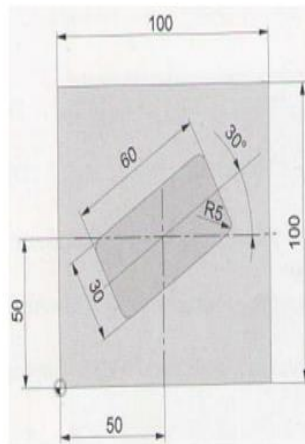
Эскиз корпуса для программирования цикла фрезерования.
